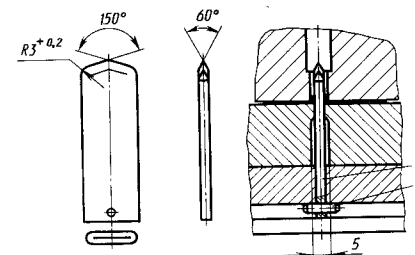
Элемент конструкции штампа для проколки и отбортовки отверстия
